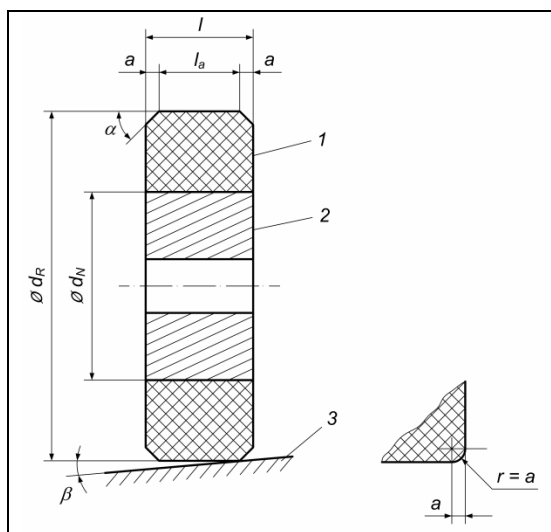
Zylindrische Laufmantelrolle mit Verkantung [16]
